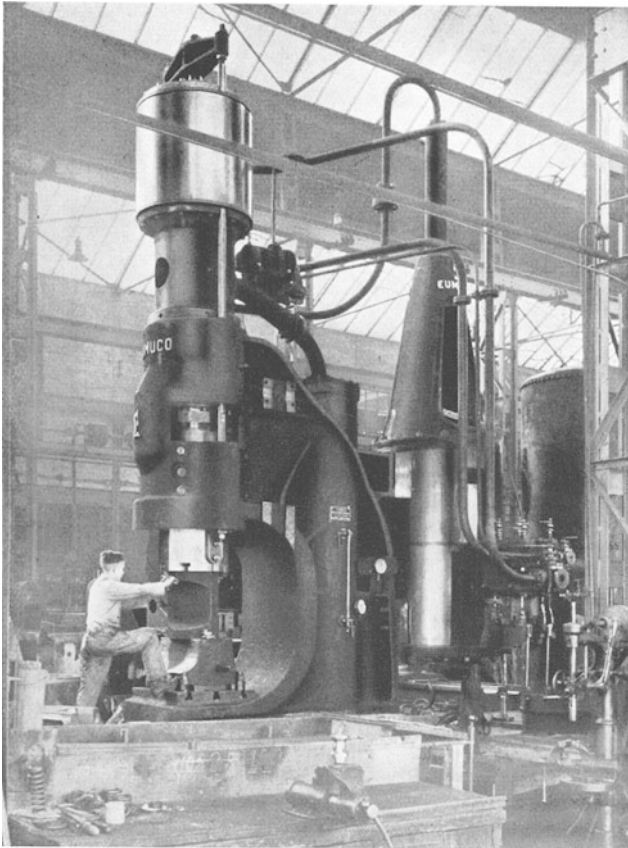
Werkstattmontage der einhüttigen Schmiedepresse (Abb. 38).
